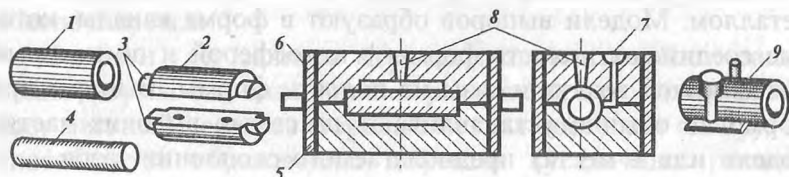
Отливка детали в разовой форме. Литейная форма из формовочной смеси: 1 — отливаемая деталь; 2 — разъемная модель; 3 — стержневые знаки модели; 4 — стержень; 5, 6 — верхняя и нижняя опоки; 7 — литниковая система; 8 — выпор; 9 — отливка
